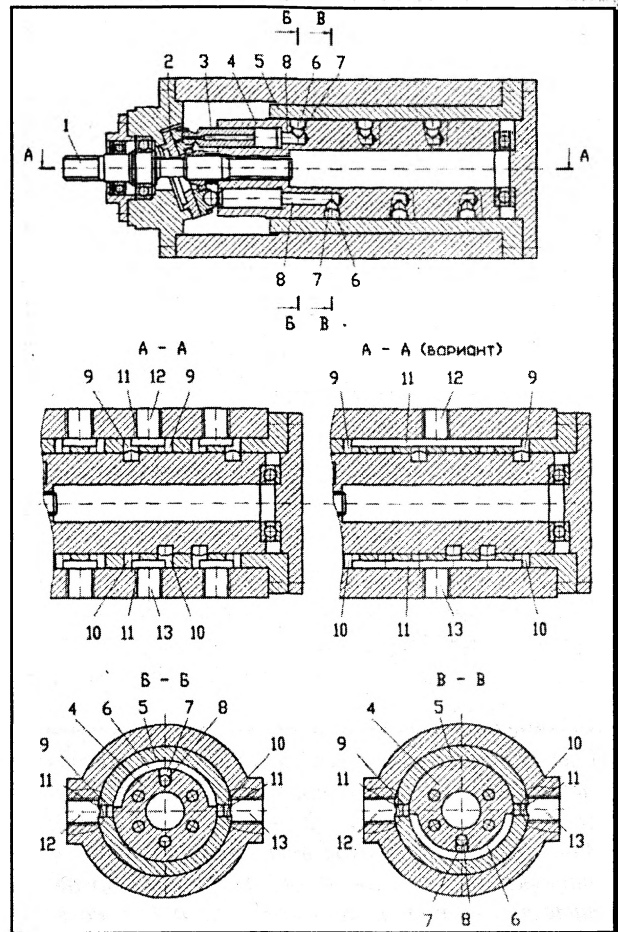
Аксиально-поршневая гидромашин с полукольцевыми пазами на образующей поверхности блока цилиндров: 1 — ведущий вал; 2 — наклонная шайба; 3 — поршень; 4 — блок цилиндров; 5 — подшипник скольжения; 6 — полукольцевые пазы; 7, 8 — каналы блока цилиндров; 9, 10 — каналы подшипника скольжения; 11 — пазы подшипника скольжения; 12, 13 — каналы корпуса гидромашин
